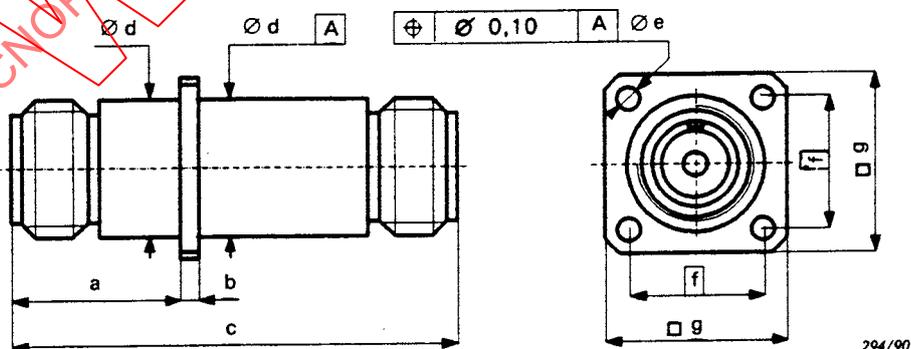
Dessin d'encombrement (pour les dimensions, voir tableau A5)
